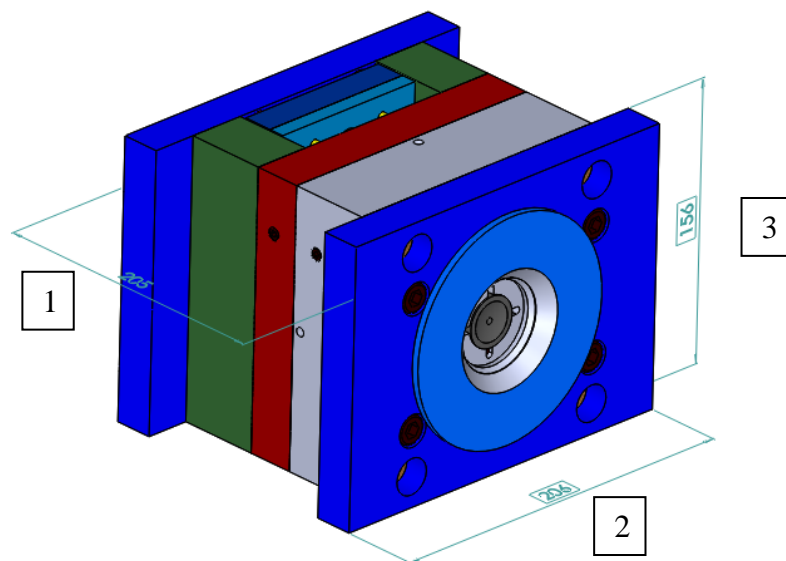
Desenho 3D do molde e dimensões, (1) altura do molde, (2) largura do molde e (3) largura placa da cavidade.
